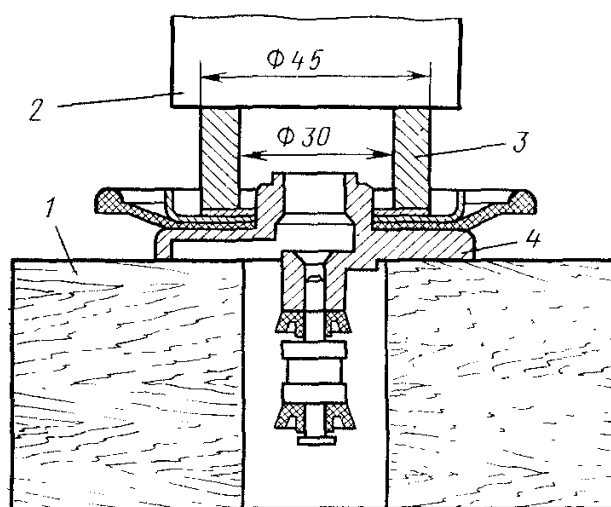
Напрессовка пластинчатой шайбы на клапан управления:
